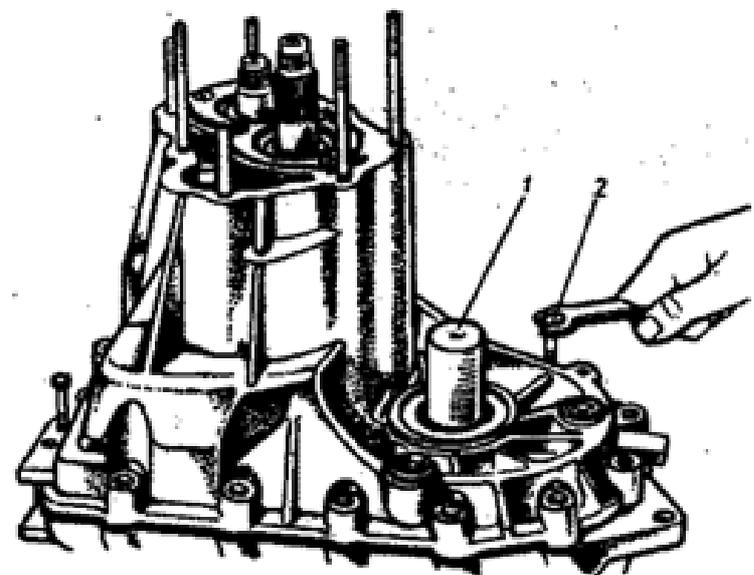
Завертывание упорных болтов в картер коробки и установка оправки в шестерню полуоси: 1 - оправка; 2 - болт
